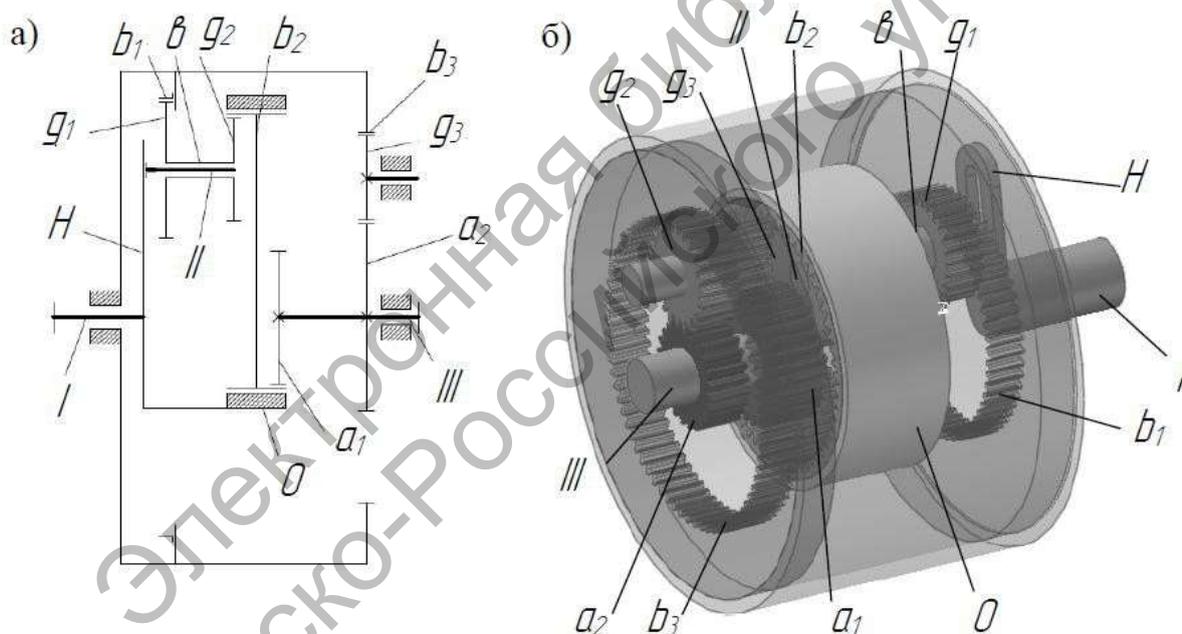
Дифференциально-замкнутый мотор-вариатор редуктор: а – кинематическая схема; б – модель; I – входной вал; II – кривошип; III – выходной вал; v – втулка; O – обойма; H – водило; g_1 – первый сателлит; g_2 – второй сателлит; g_3 – вспомогательное колесо; b_1 – опорное колесо; b_2 – колеса с внутренним зацеплением вспомогательной ступени; a_1 – центральное колесо; a_2 – вспомогательное центральное колесо
